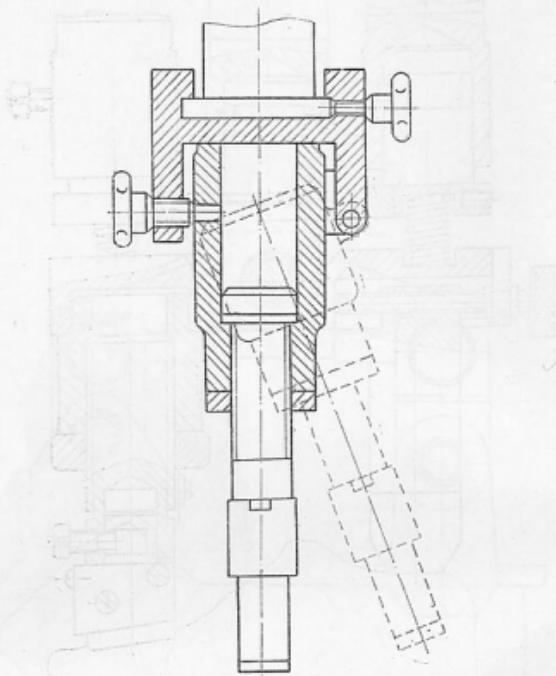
Чертеж откатной паточного для обрабки с коническим загленищем.
